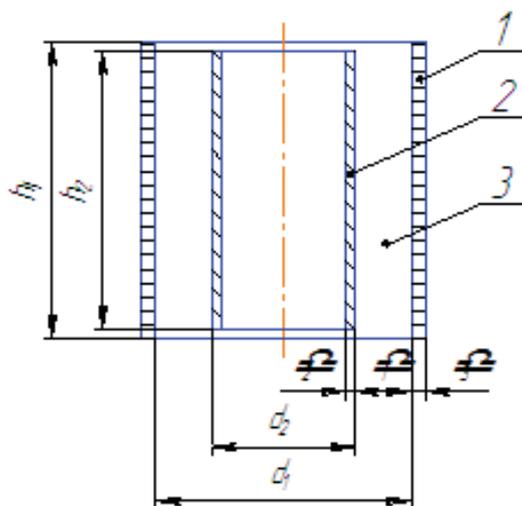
Эскиз цилиндрического индуктора: 1 – индуктор, 2 – нагреваемое изделие, 3 – зазор
